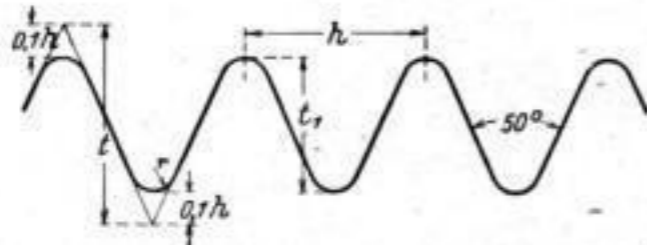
Profil des Müller & Schweizer-Gewindes
